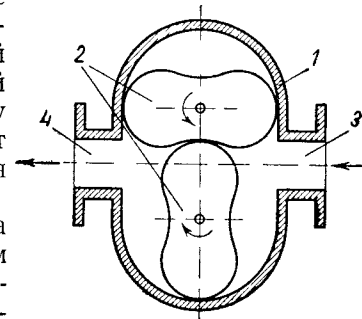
Устройство бесшмазочного двухроторного насоса: 1 — корпус, 2 — роторы, 3 — впускной патрубок, 4 — выпускной патрубок
